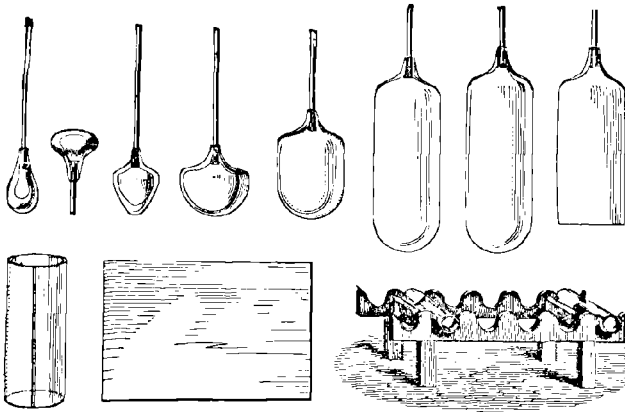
Formes successives que prend le verre soufflé pour devenir carreau de verre.
